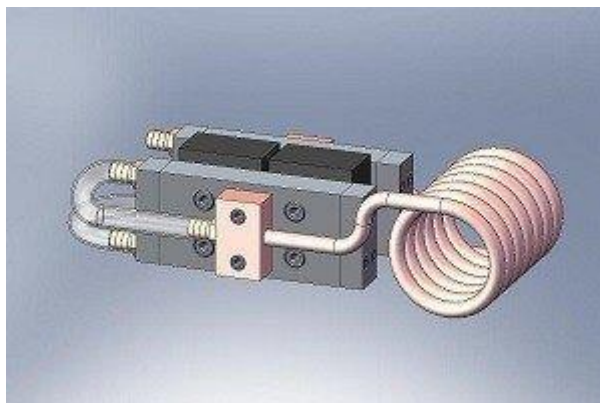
Індукційний нагрівач для закручування стрічкової заготовки
